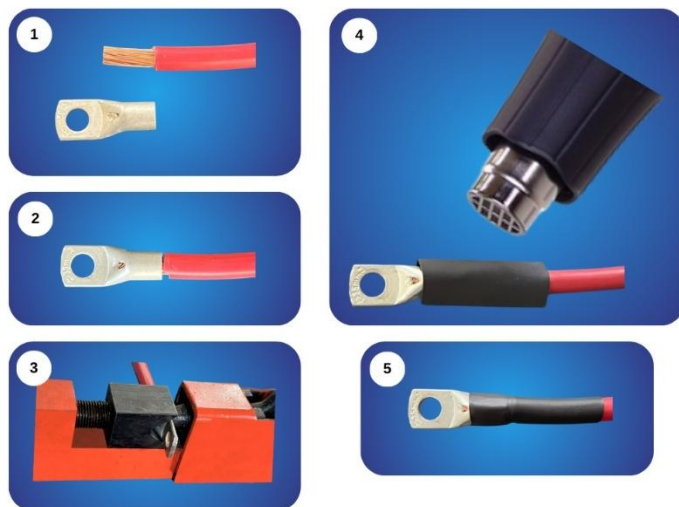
Montagem do Cabo com Terminal de Compressão TM.
